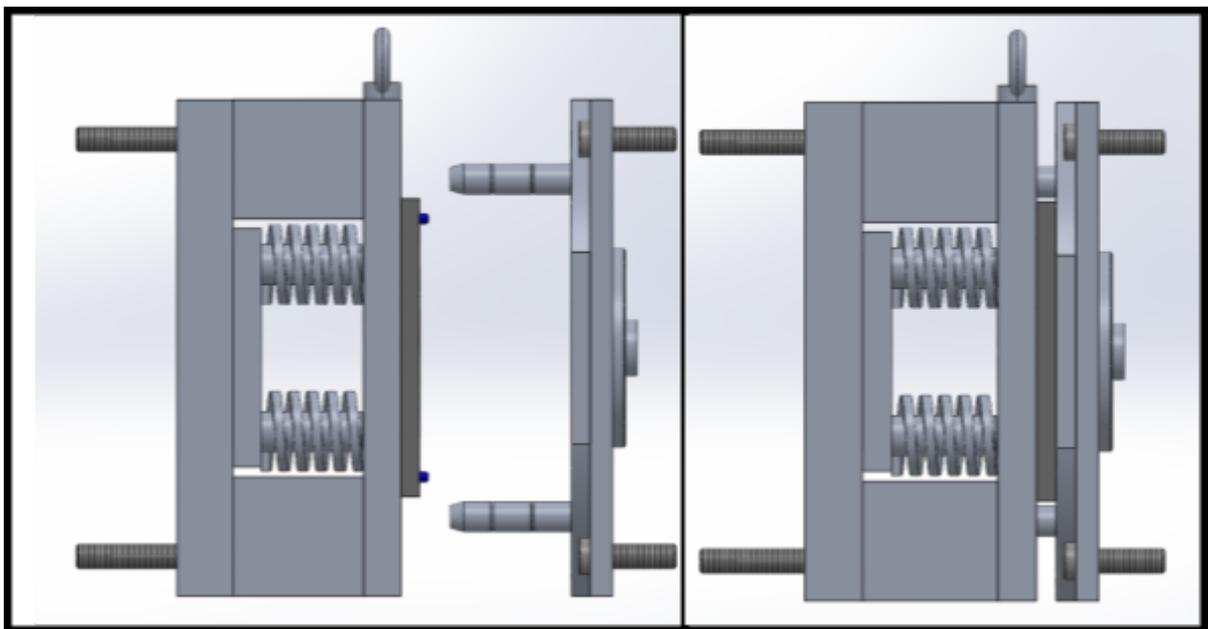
M. Molde montado en el portamolde (Vista lateral)
